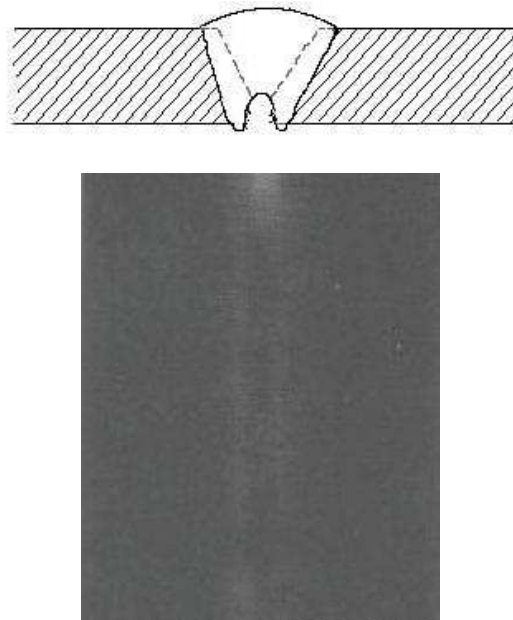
Junta soldada con concavidad interna.
